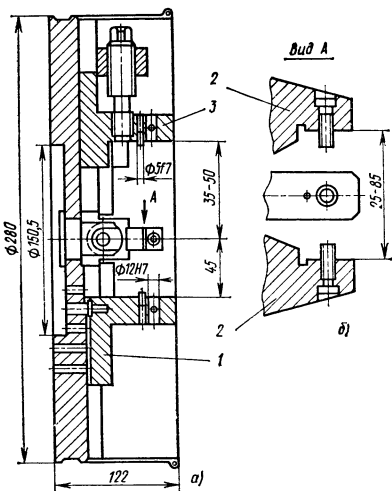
Патрон четырехкулачковый для обработки штуперов:
